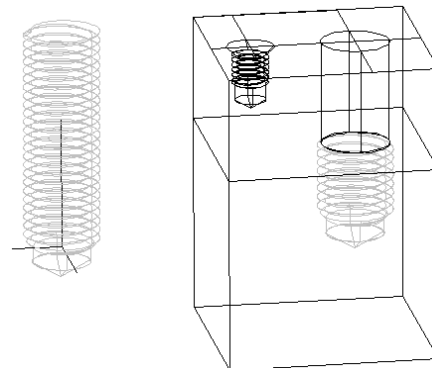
Резьбовое отверстие под шпильку
